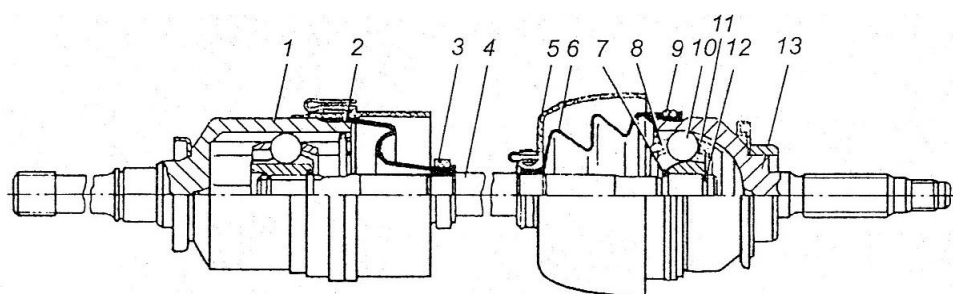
Карданная передача с шарнирами равных угловых скоростей: 1 – корпус внутреннего шарнира; 2 – фиксатор внутреннего шарнира; 3,9 – хомут крепления чехла; 4 – вал привода передних колес; 5 – защитный кожух чехла; 6 – гофрированный защитный чехол; 7 – упорное кольцо обоймы; 8 – сепаратор; 10 – шарик; 11 – обойма; 12 – стопорное кольцо обоймы; 13 – корпус наружного шарнира
